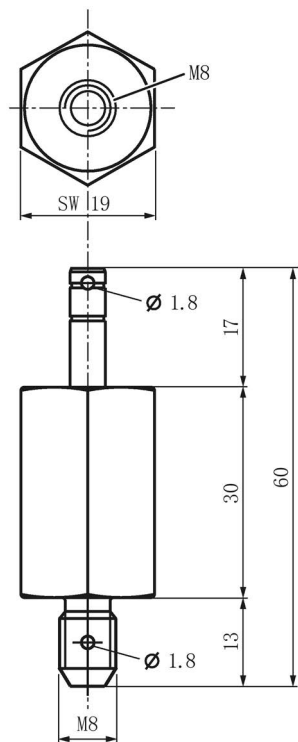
快速更换夹具 6GT2690-0AH00 的尺寸图
